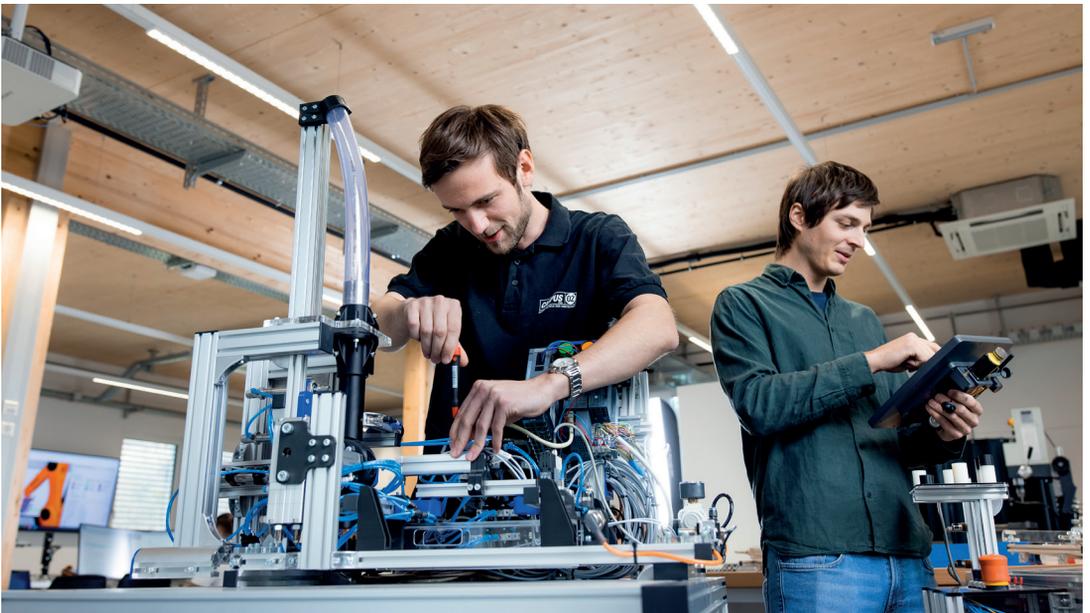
Prototyp-Aufbau einer Richtmaschine für Drahtelemente im Rapid Prototyping Lab.
